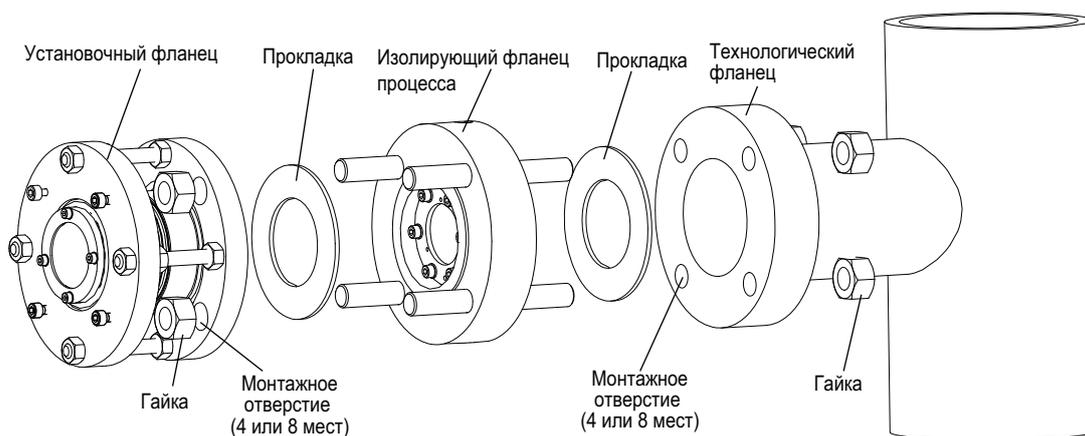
Установка изолирующего фланца процессса и установочного фланца
